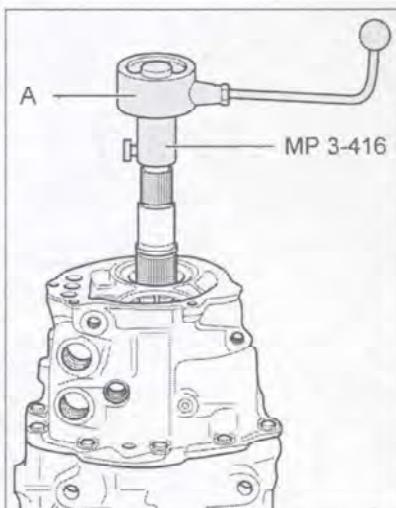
Измерьте момент сил трения роликоподшипников вторичного вала с помощью стандартного инструмента (A).
